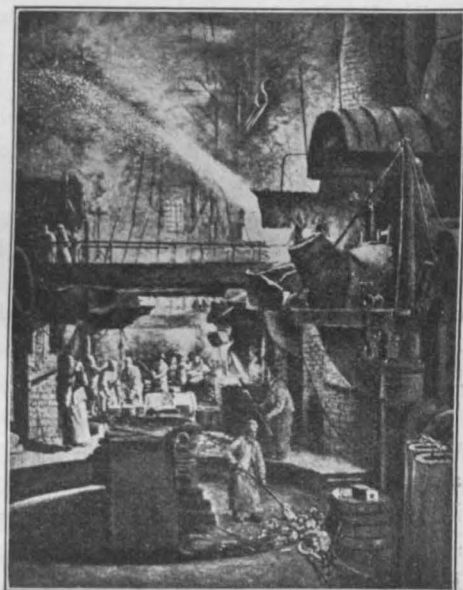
Im Bessemerwerk der Firma Krupp-Essen.
